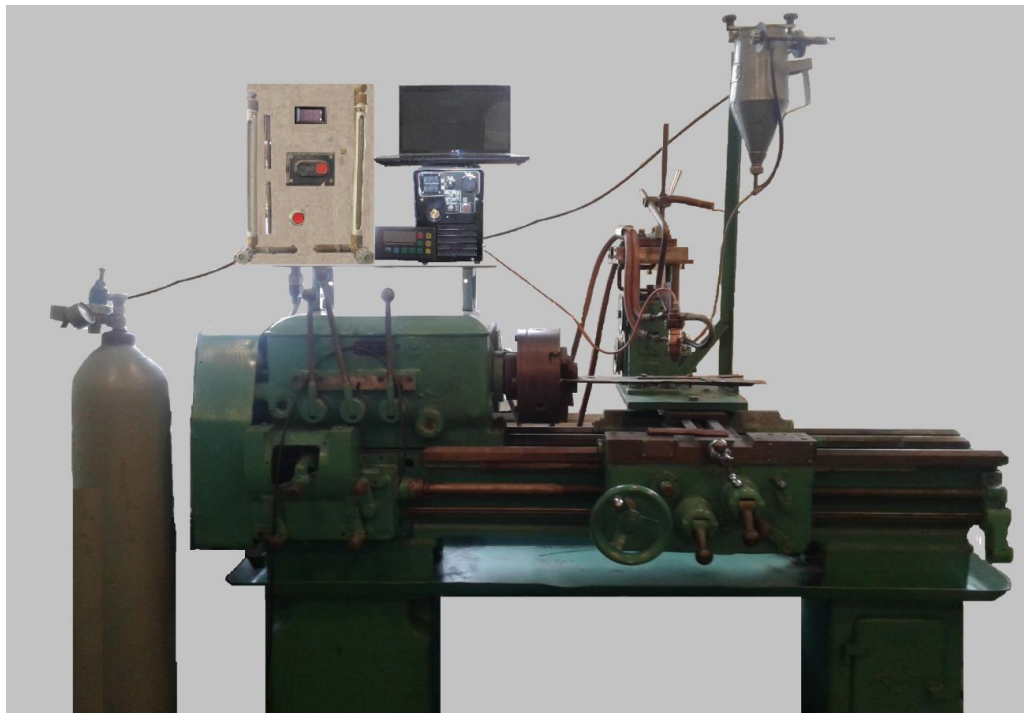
Установка для плазмового наплавлення: 1 – блок управління; 2 – коливальний механізм; 3 – порошковий живильник; 4 – плазмотрон; 5 – токарно-гвинторізний верстат DEG; 6 – балон з аргоном
